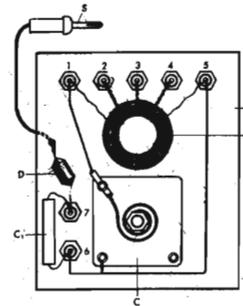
Montaggio dei particolari (Pannello frontale visto dal di sotto).
